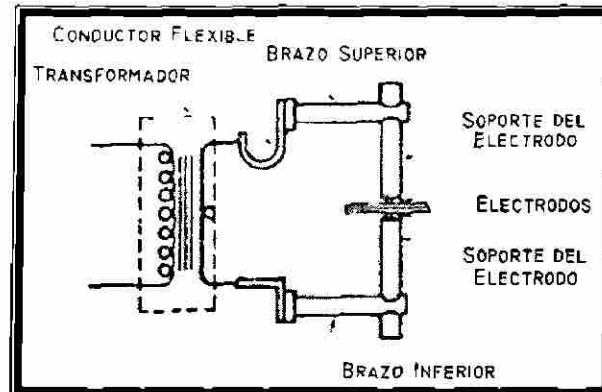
Componentes del circuito eléctrico de una máquina soldadora por puntos [69, 72].
